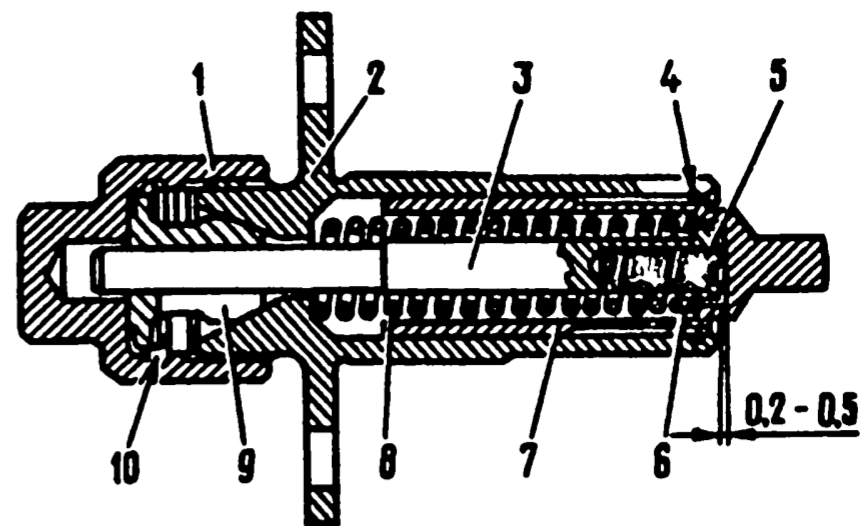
Разрез натяжителя цепи: 1 - колпачковая гайка; 2 - корпус натяжителя; 3 - стержень; 4 - пружинное кольцо; 5 - пружина плунжера; 6 - шайба; 7 - плунжер; 8 - пружина; 9 - сухарь; 10 - пружинное кольцо
